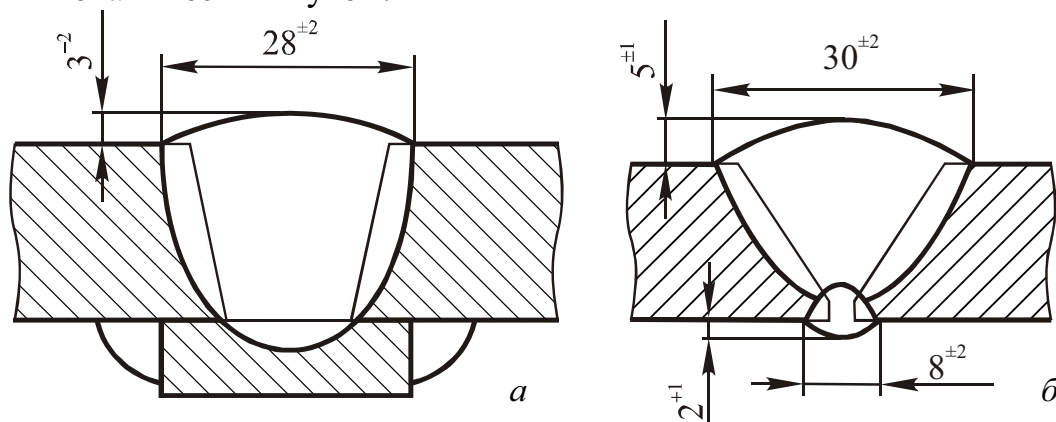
Конструктивные элементы сварных швов:
